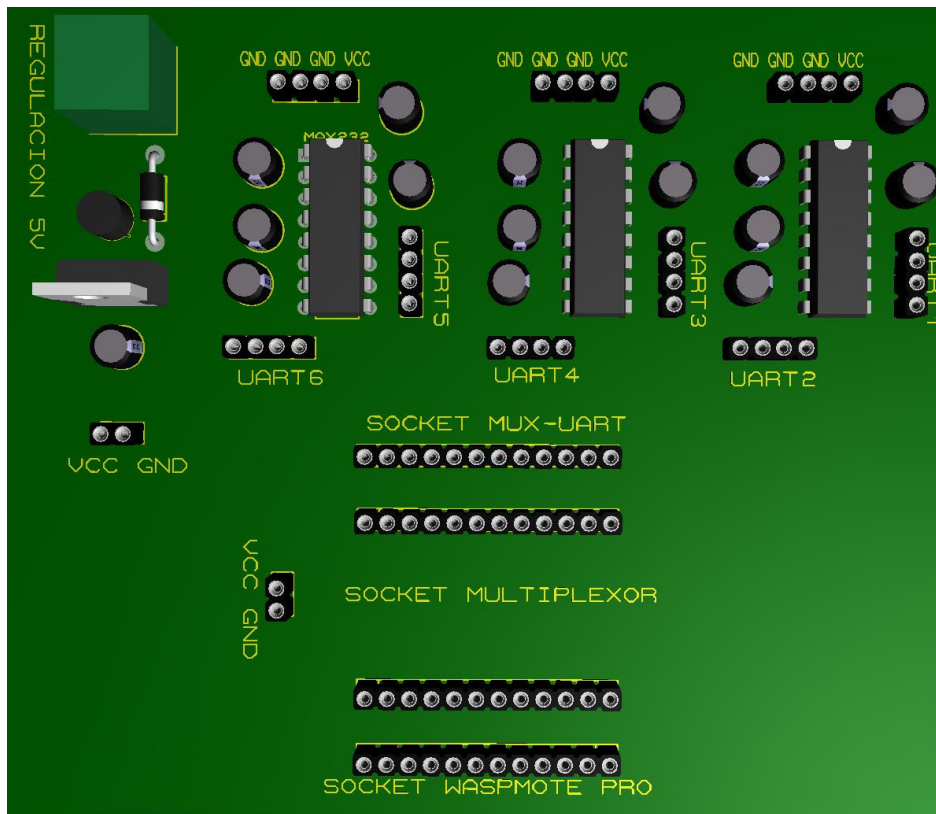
Diseño de PCB para la interconexión de dispositivos.
